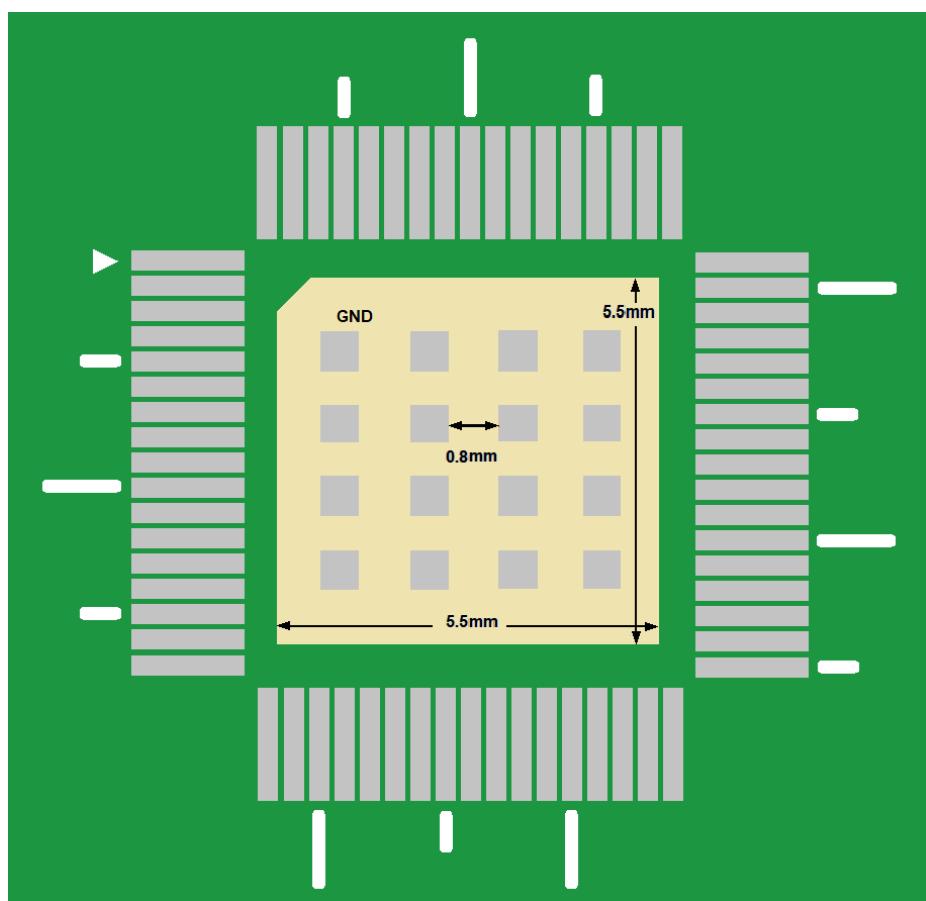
LT168B 底部焊盘 PCB 的设计建议-1
